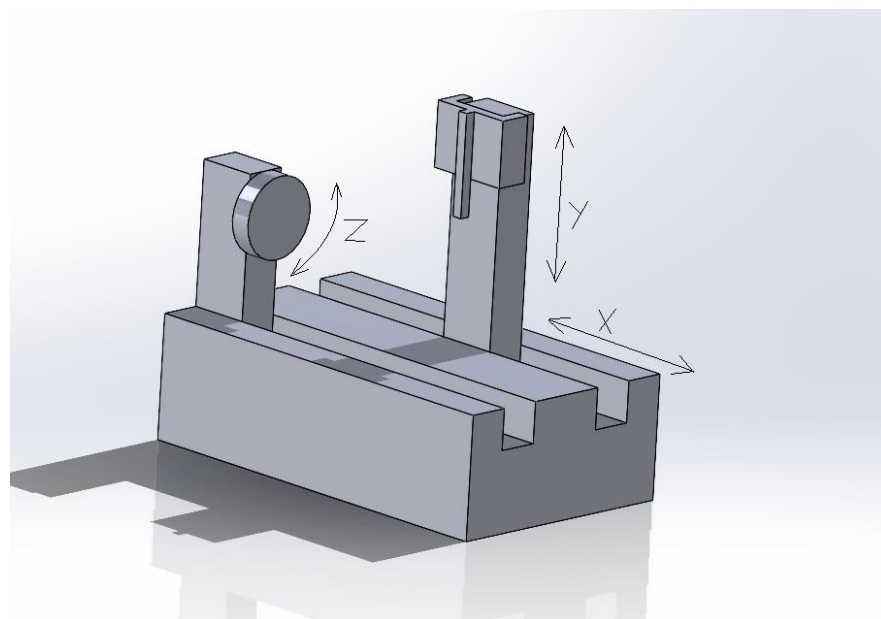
Компонівка з рухомою заготовкою , та рухомим порталом
